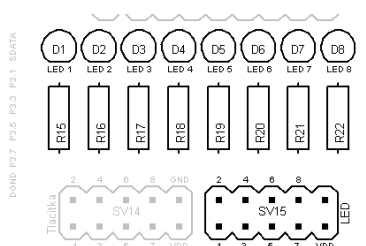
Rozmístění součástek a popis desky - tlačítka
